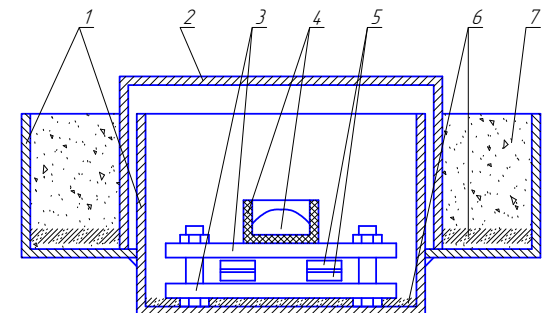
Схема размещения образцов для пайки в контейнере с затвором из песка: 1 – корпус; 2 – крышка; 3 – струбцина; 4 – графитовый тигель с навеской цинка; 5 – нахлесточные образцы с припоем из меди М1; 6 – карбюризатор; 7 – песок
